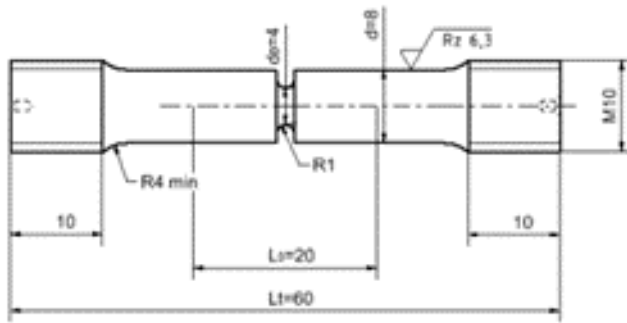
Gekerbte Rundzugprobe Kerbradius 1 mm RzR1
